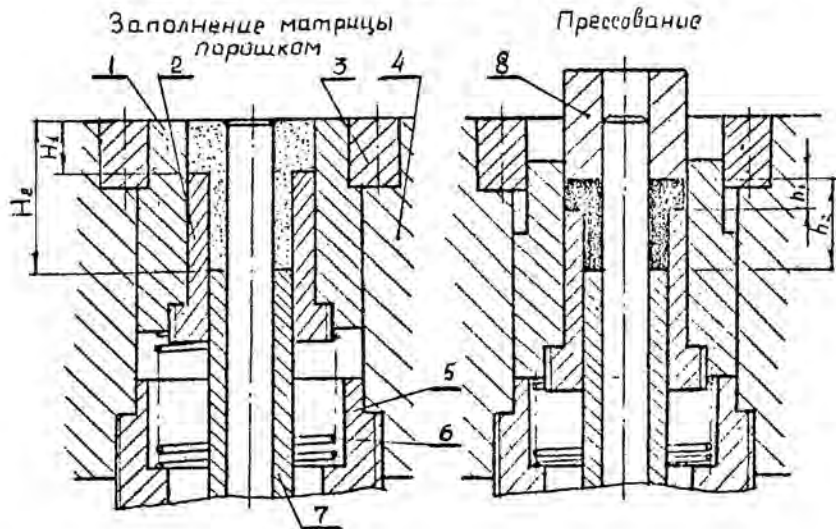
Схема прессформы для прессования втулок с наружным верхним буртом:
